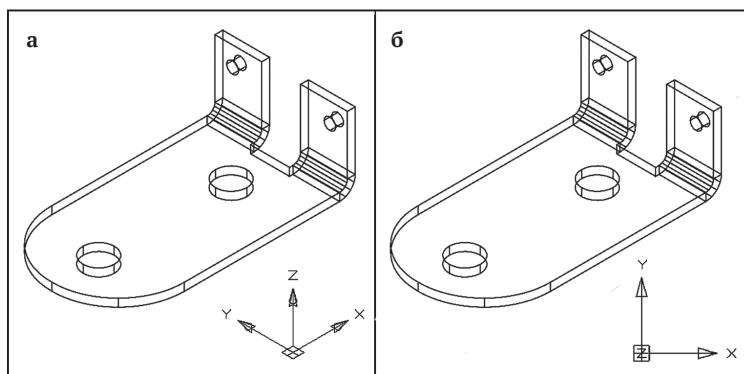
Подготовка 3D-модели детали «Уголок» для вставки ее изображения в 2D-чертеж (визуальный стиль «Каркас»)
